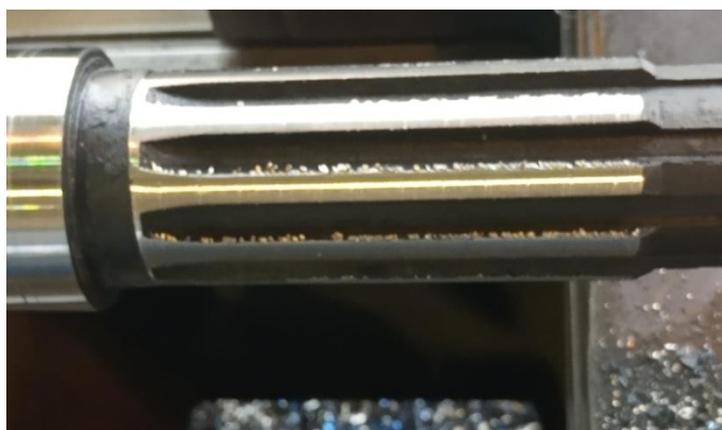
Обработка ударным воздействием на вал  $\varnothing 60$  с длиной обрабатываемой зубчатой поверхности 70 мм из стали марки 12ХН3А
